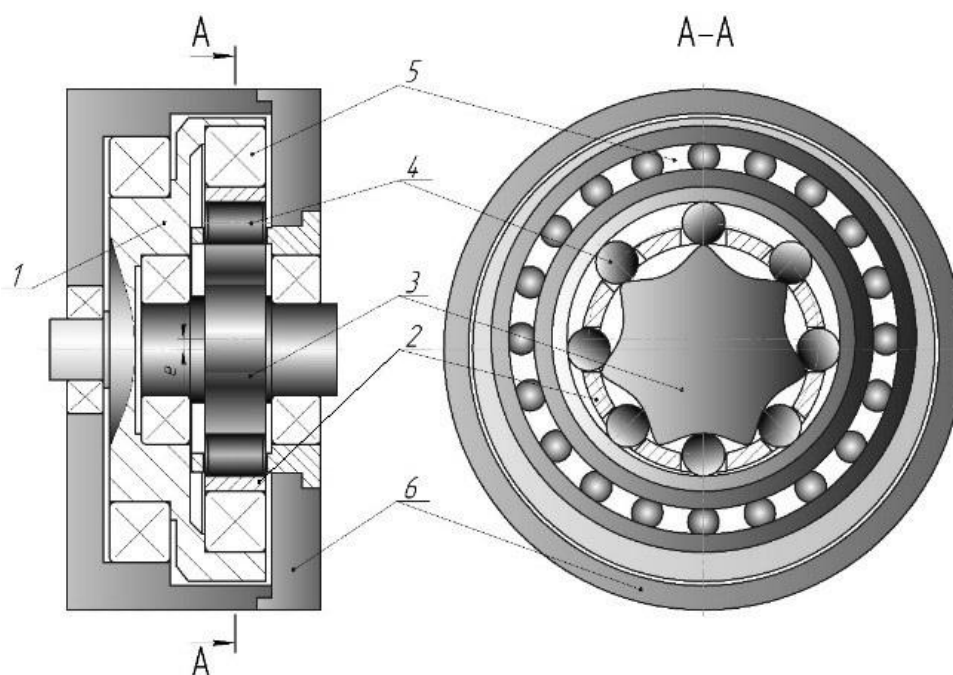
Плоская радиальная передача с промежуточными телами качения. 1 – генератор волн, 2 – сепаратор, 3 – профильное колесо, 4 – промежуточные тела качения, 5 – подшипник качения, 6 – корпус механизма
